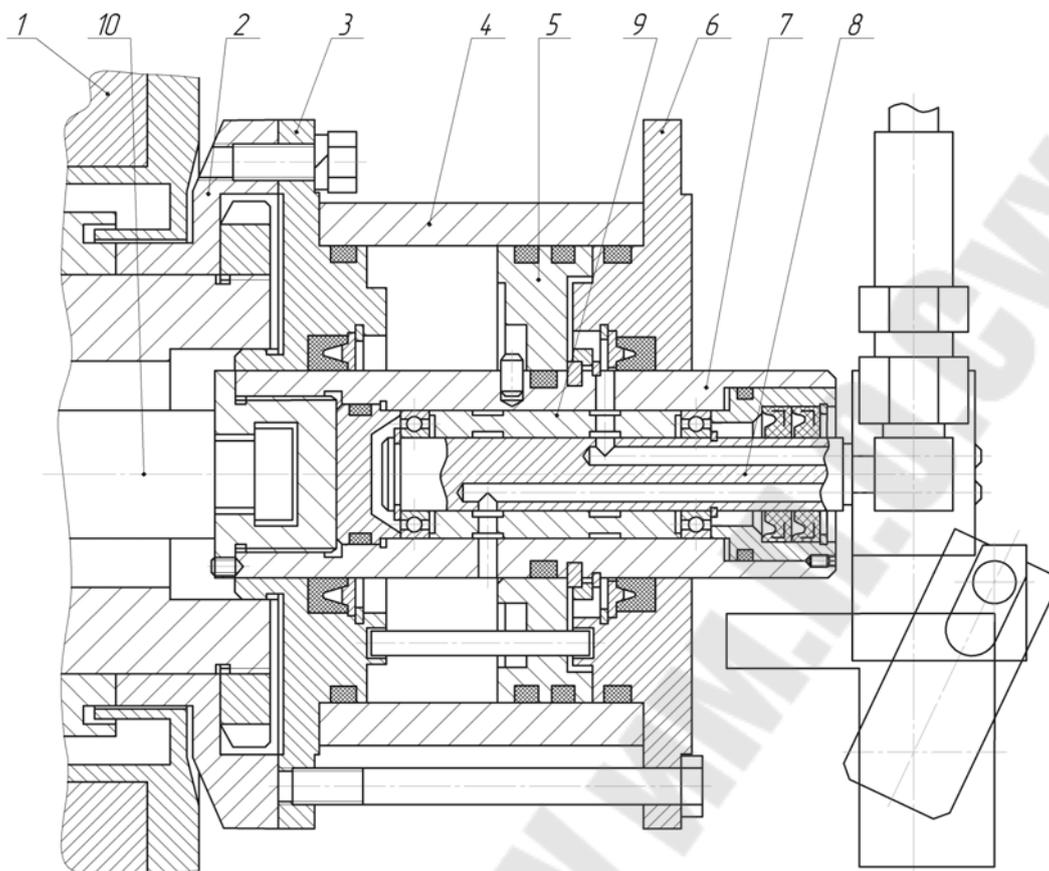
цилиндр зажима обрабатываемой детали: 1 – станина; 2 – фланец; 3,6 – крышка; 4 – гильза; 5 – поршень; 7 – шток; 8 – коллектор; 9 – втулка; 10 – тяга
